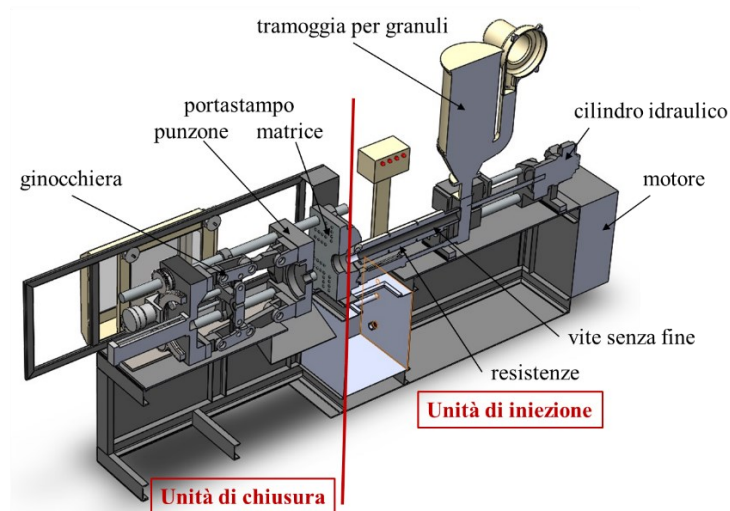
Schema di una macchina di stampaggio ad iniezione
